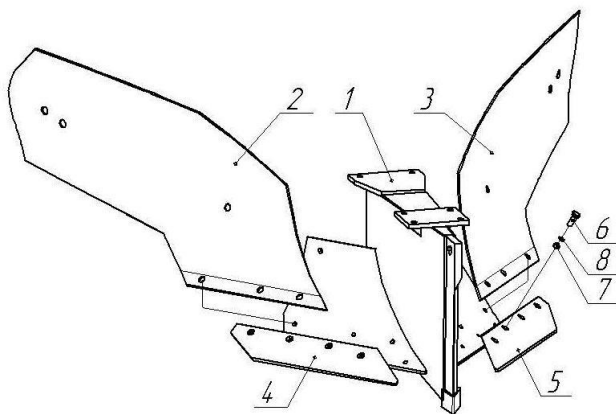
ПКЛ 70.02.000 Корпус с отвалами и лемехами
